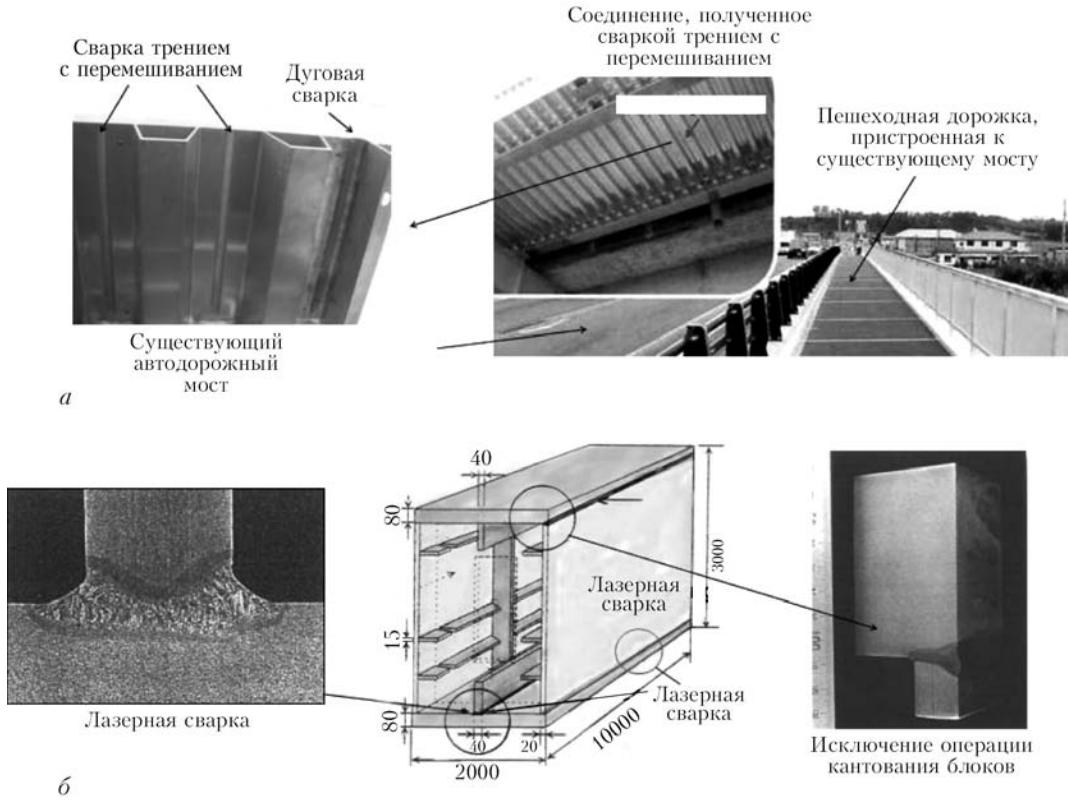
Применение сварки трением с перемешиванием для получения элемента моста (а) и концепция использования лазерной сварки (б)
